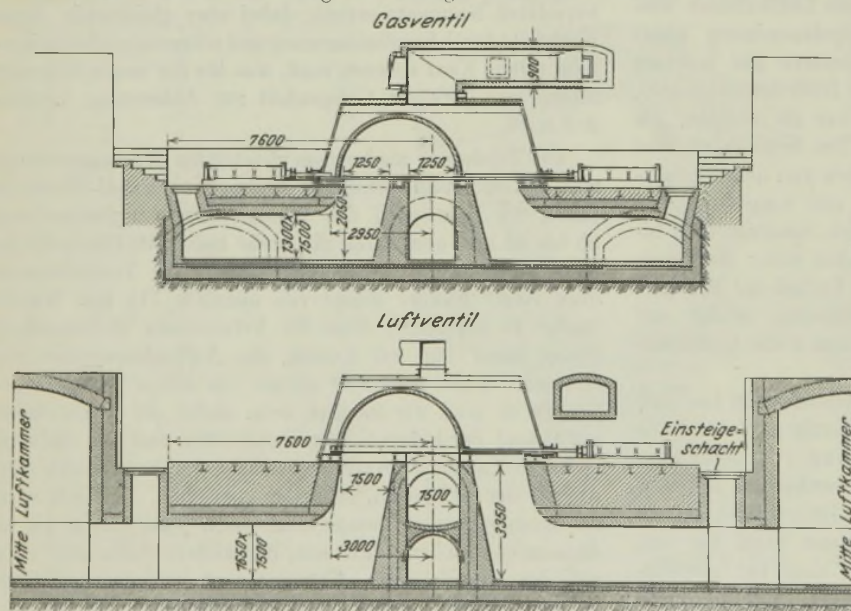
Luftgekühltes Umstellventil mit Betätigung durch Druckluftzylinder.
